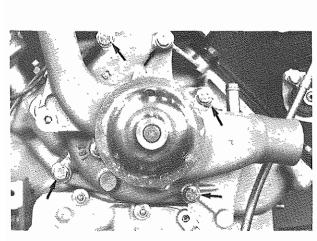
Viti fissaggio pompa acqua Water pump screws
